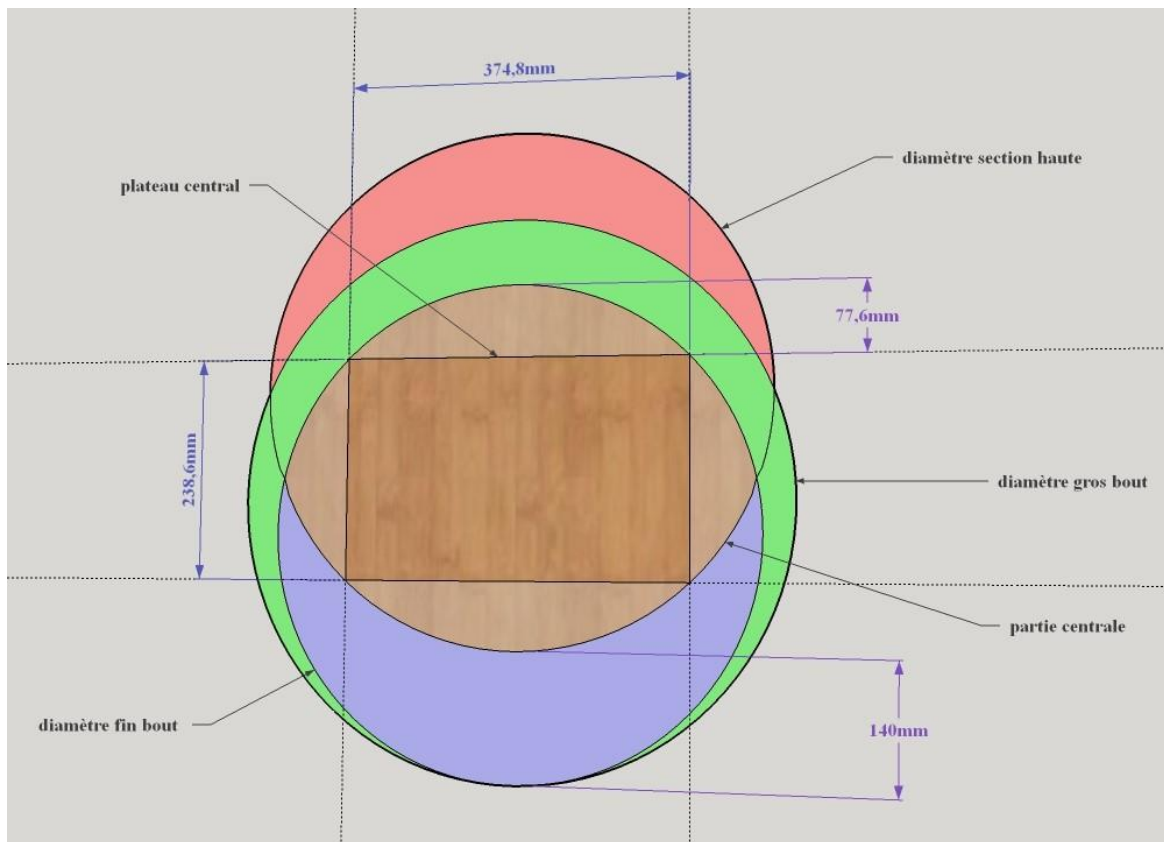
Equarrissage de la bille N° 1 et dimensions du plateau centrale (Takoudjou, 2020)
